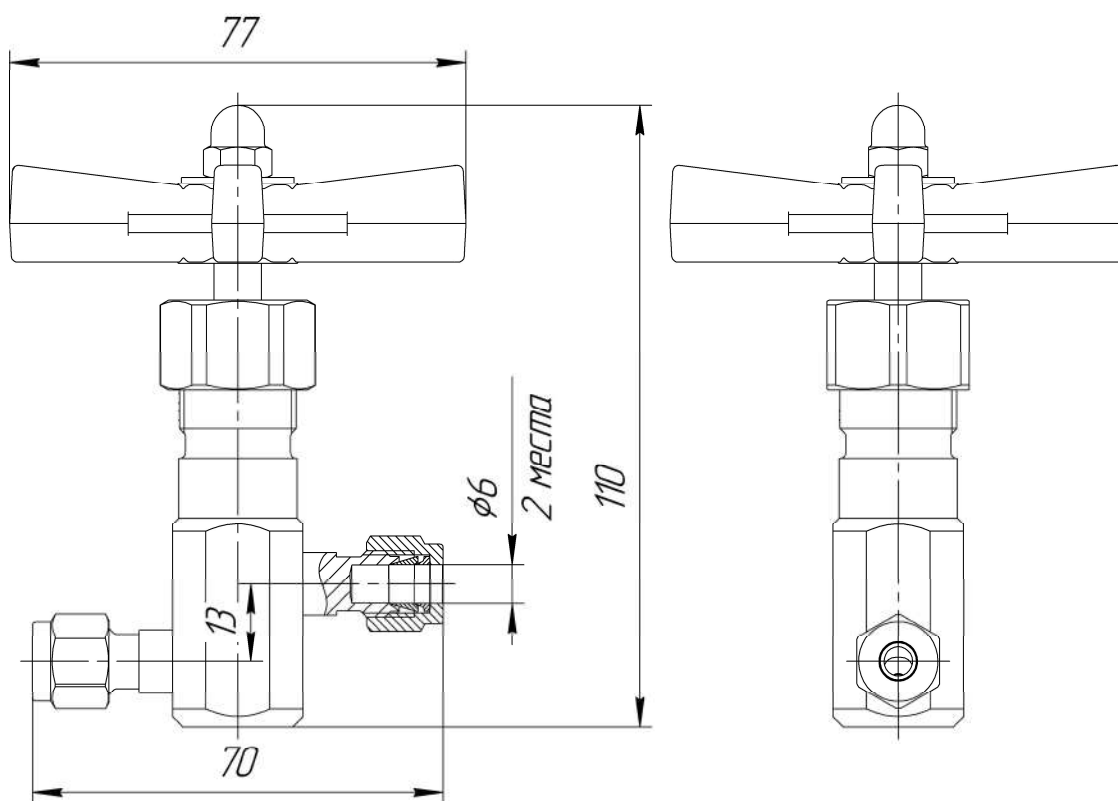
Габаритно-присоединительные размеры ДРР25-Н6М6М
